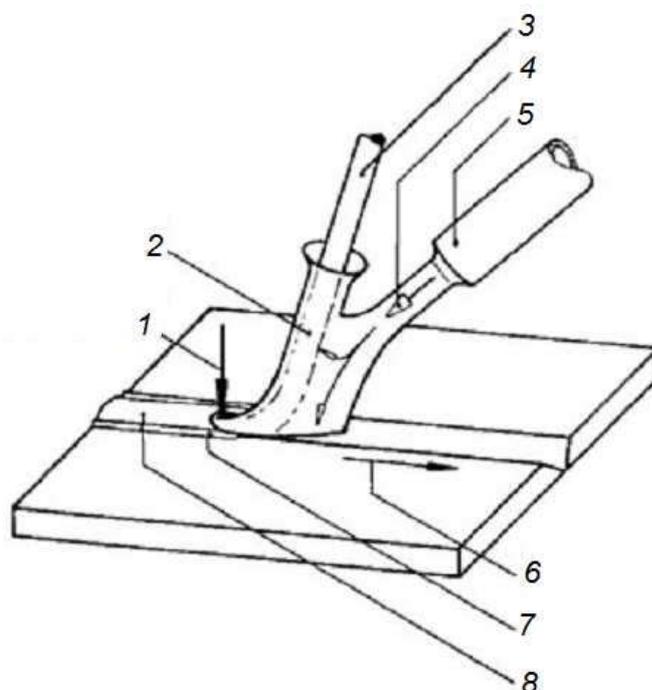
Приспособление для сварки пластмасс:
